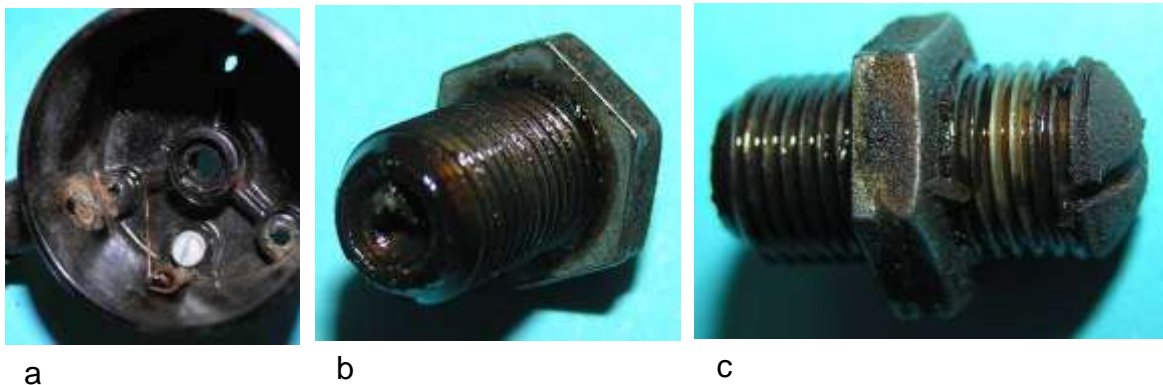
Einstellschraube des Axiallagers: a) Gehäusekopf mit zentraler Gewindebohrung, b) Sitz der Kugel, c) Schlitzschraube und Kontermutter
